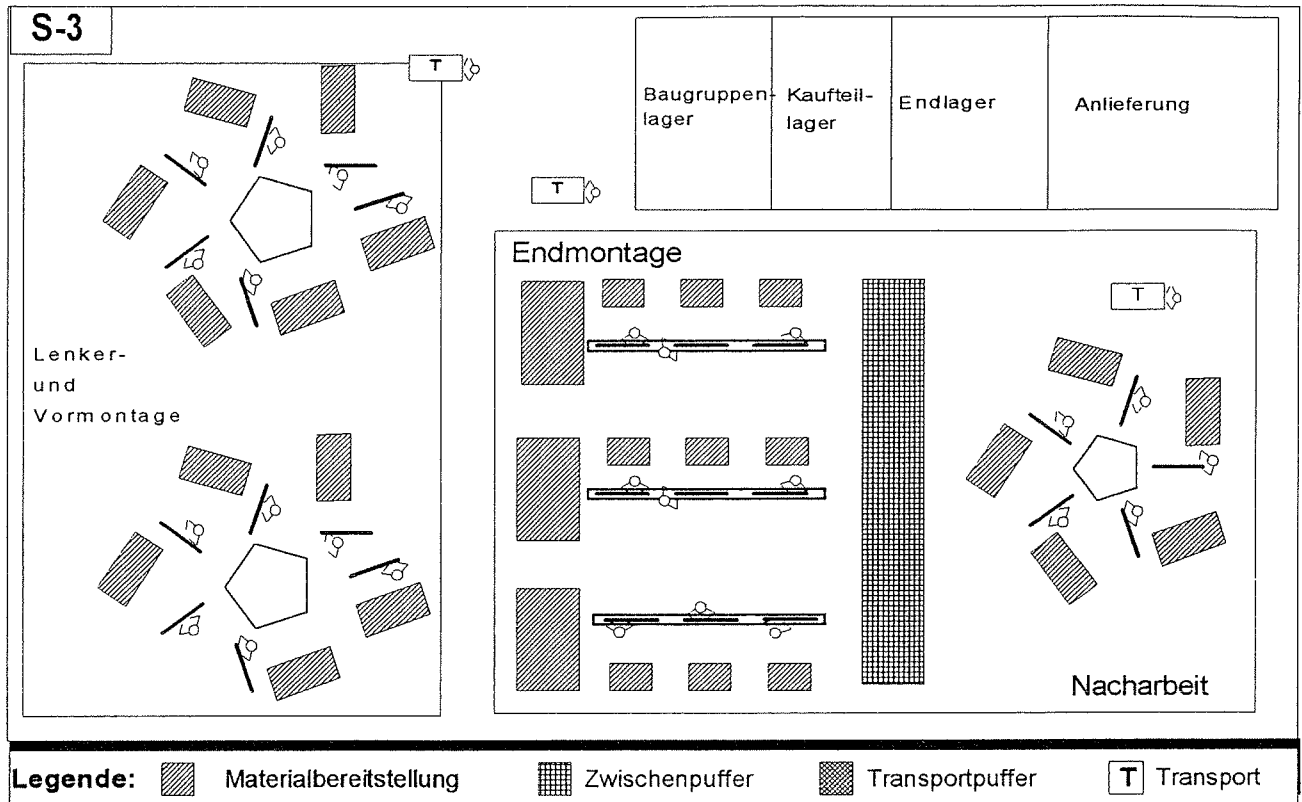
Layout der Variante Fahrradfabrik (S-3)
